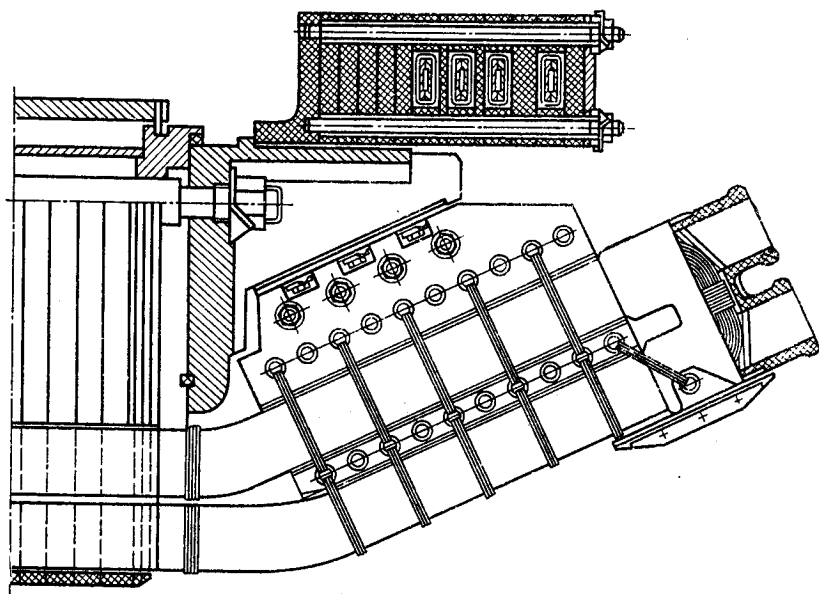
Крепление лобовых частей обмотки статора генератора ТГВ-300
